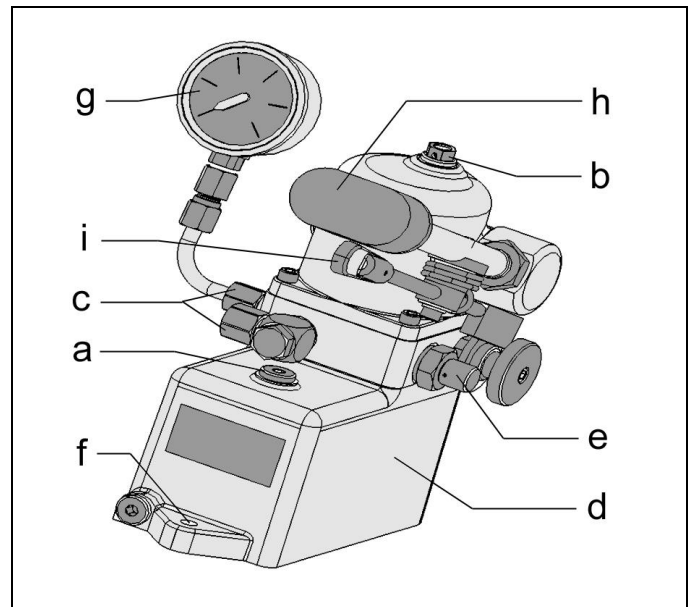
Vue d'ensemble des composants (figure de principe 8806, 8807)
